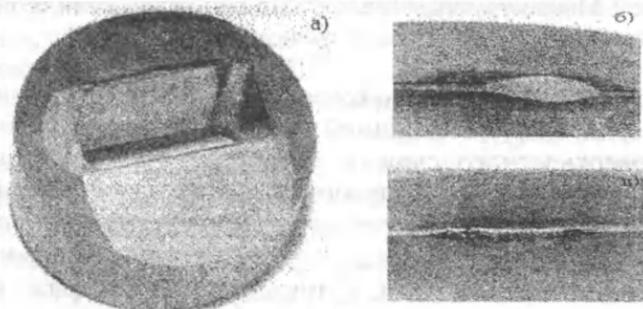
Внешний вид обсечного пуансона (а); характер усталостного разрушения режущей кромки (б) и износа рабочей поверхности (в).
